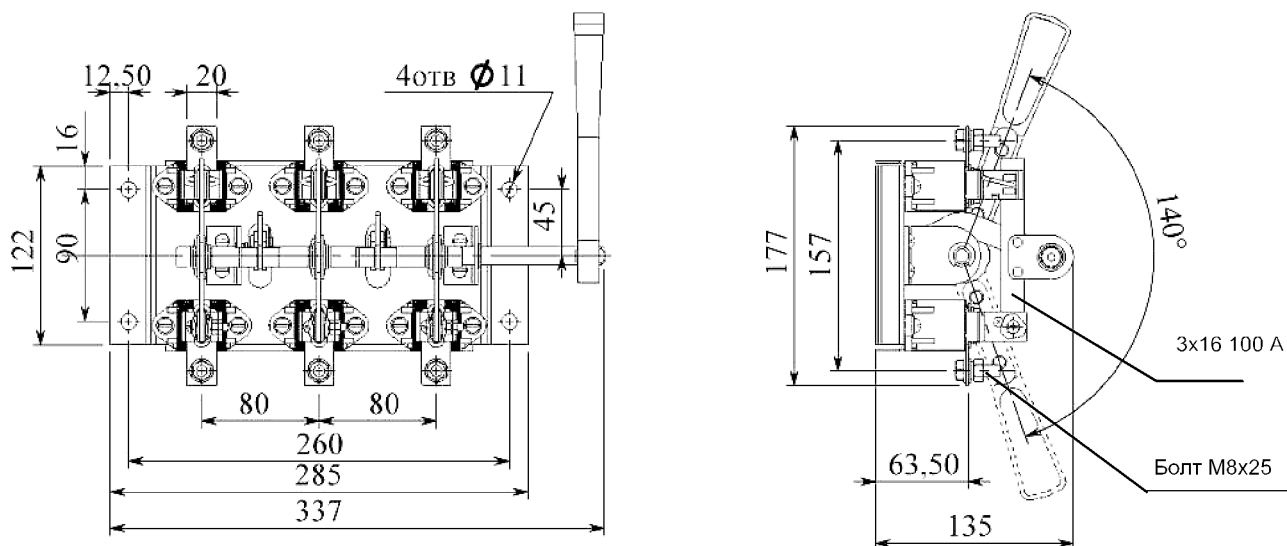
Разъединитель PE19 трехполюсный с боковой рукояткой, переднего присоединения шин
